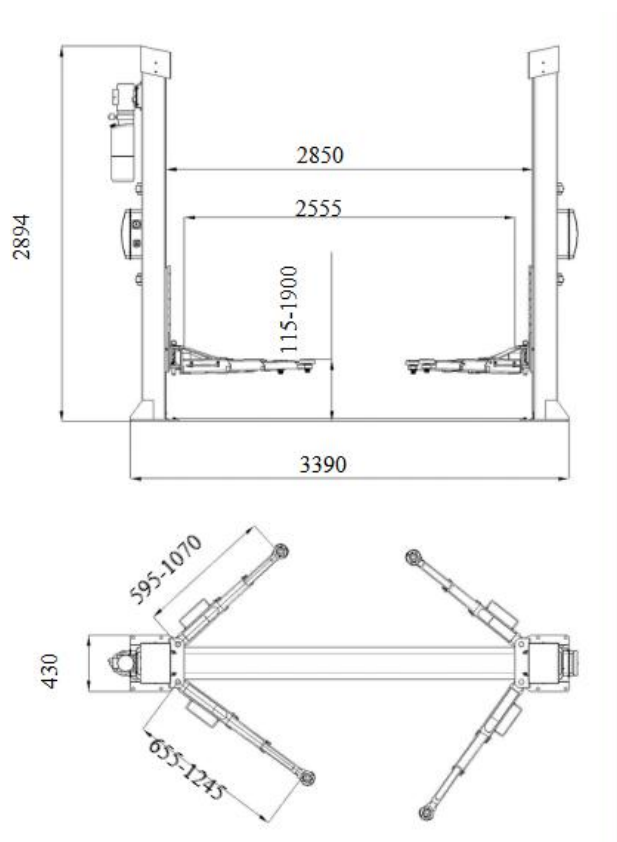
Dimensioni esterne sollevatore (unità: mm)
